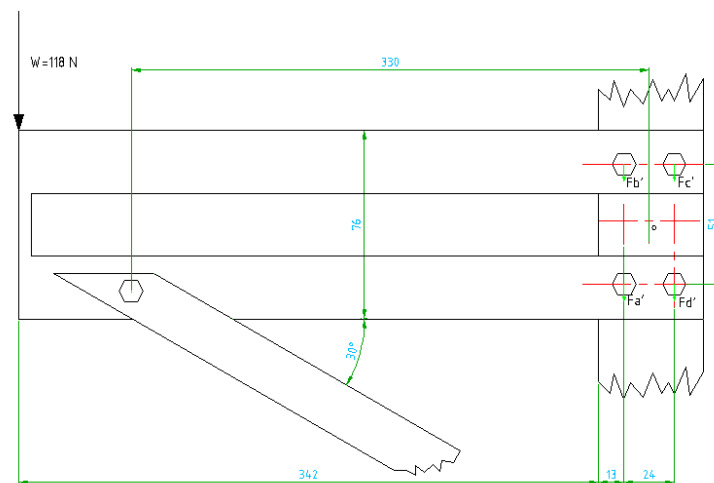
Distribución de las cargas aplicada sobre el perfil.
